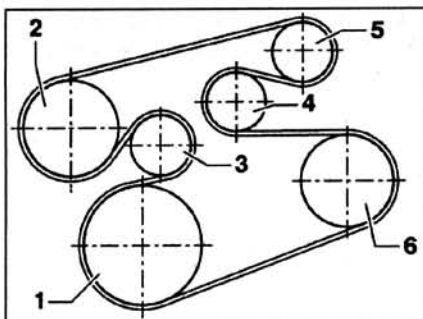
б. Схема установки ремня привода на автомобилях с компрессором кондиционера.
